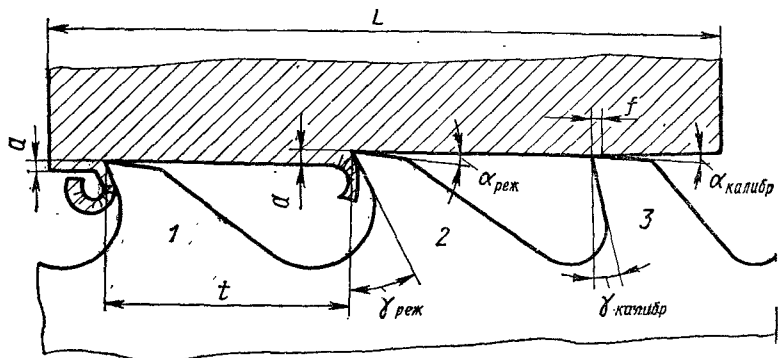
Режущие (1 и 2) и калибрующие (3) зубья протяжки
